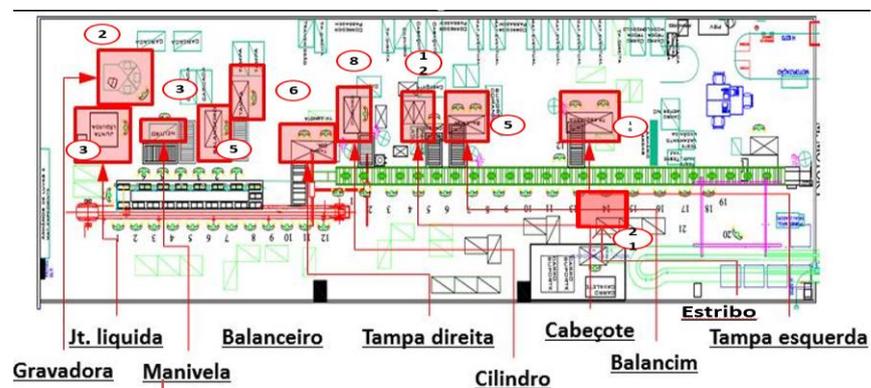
Layout* produtivo de uma linha de Montagem do Motor
